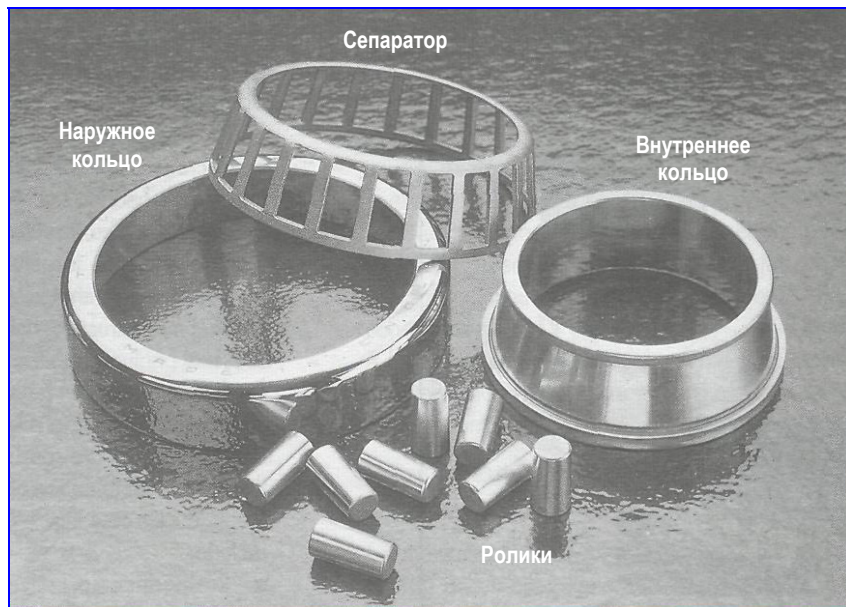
Составные части однорядного конического роликового подшипника (тип TS).
